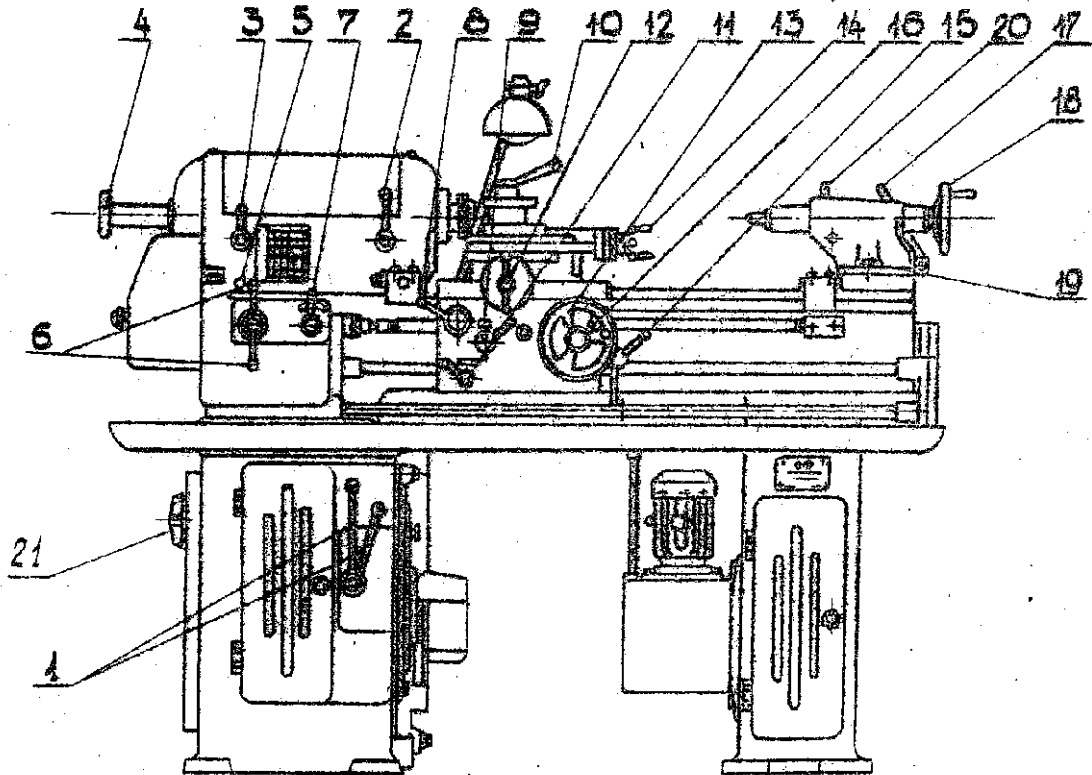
Токарно-винторезный станок ТВ – 320 (органы управления).
